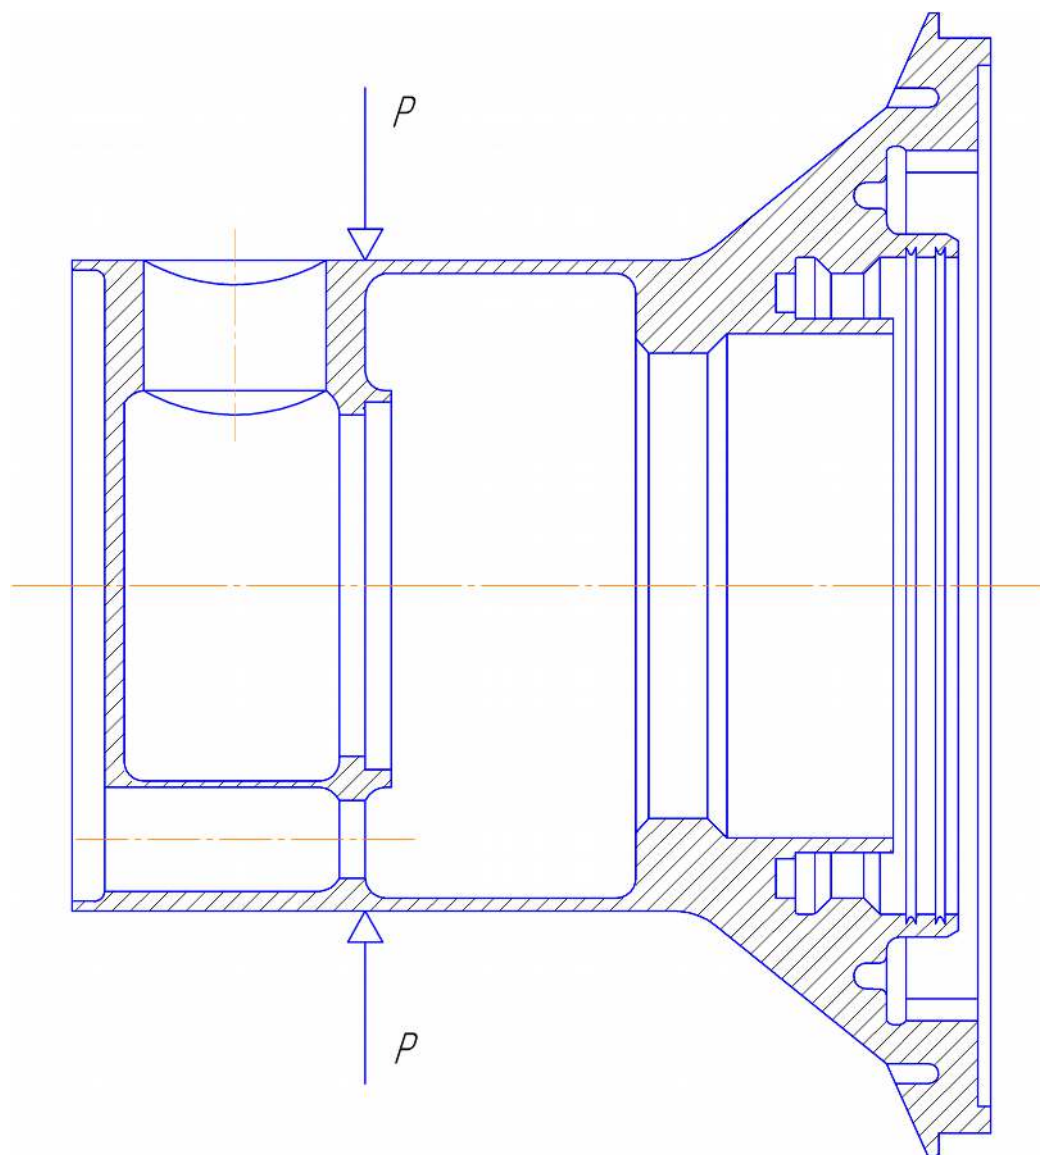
Схема базирования заготовки в схвате промышленного робота
